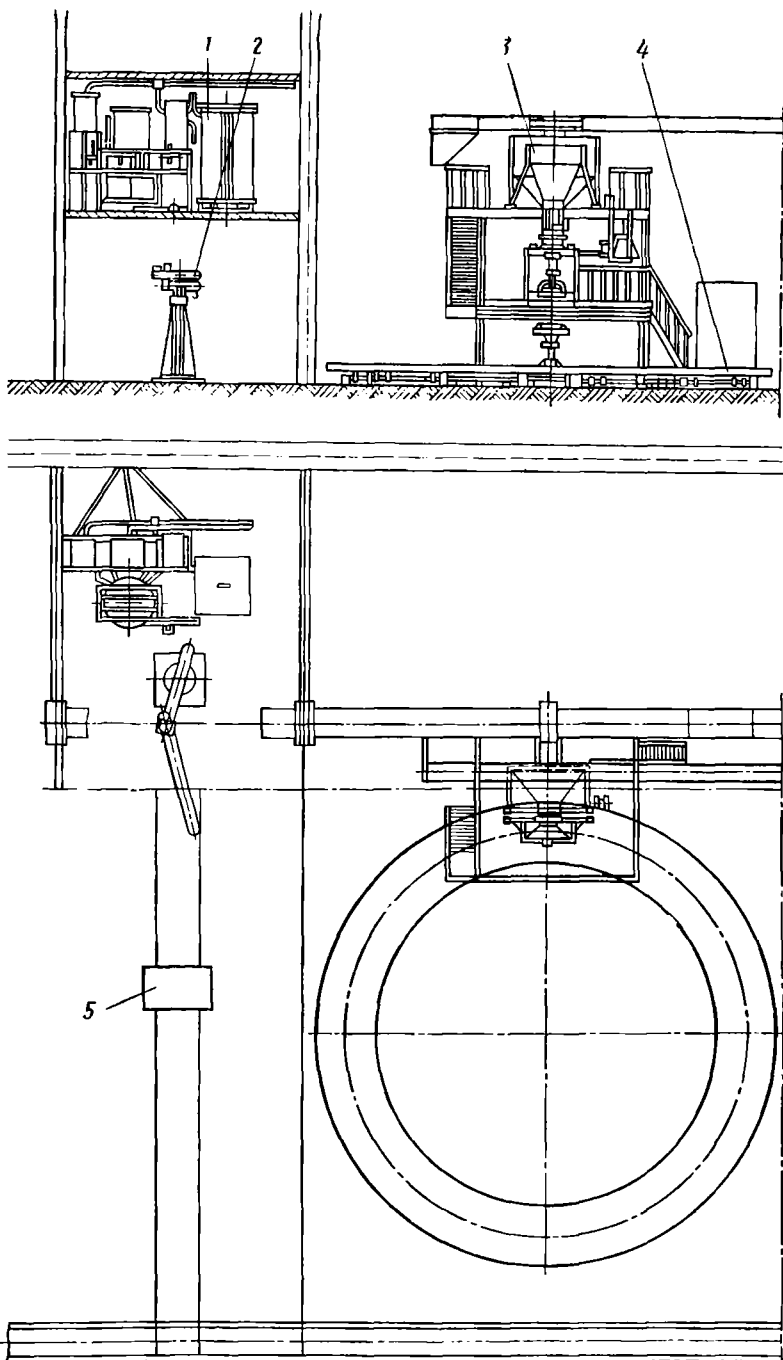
Схема механизированного участка для изготовления стержней из жидких смесей
